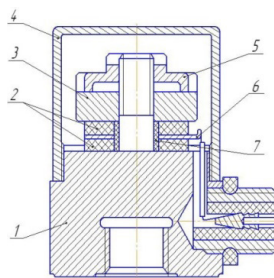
Вибропреобразователь ДН4: 1 – корпус; 2 – пьезокристалл; 3 – грузик; 4 – колпачок; 5 – гайка; 6 – вывод; 7 – трубка
